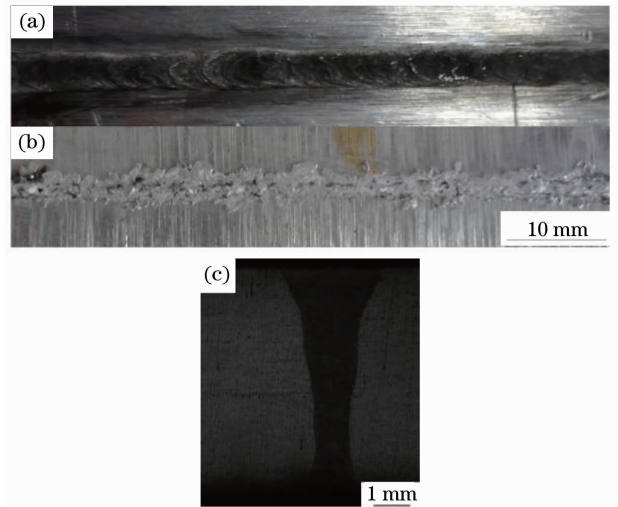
焊缝宏观形貌。(a) 上表面;(b) 下表面;(c) 横截面
